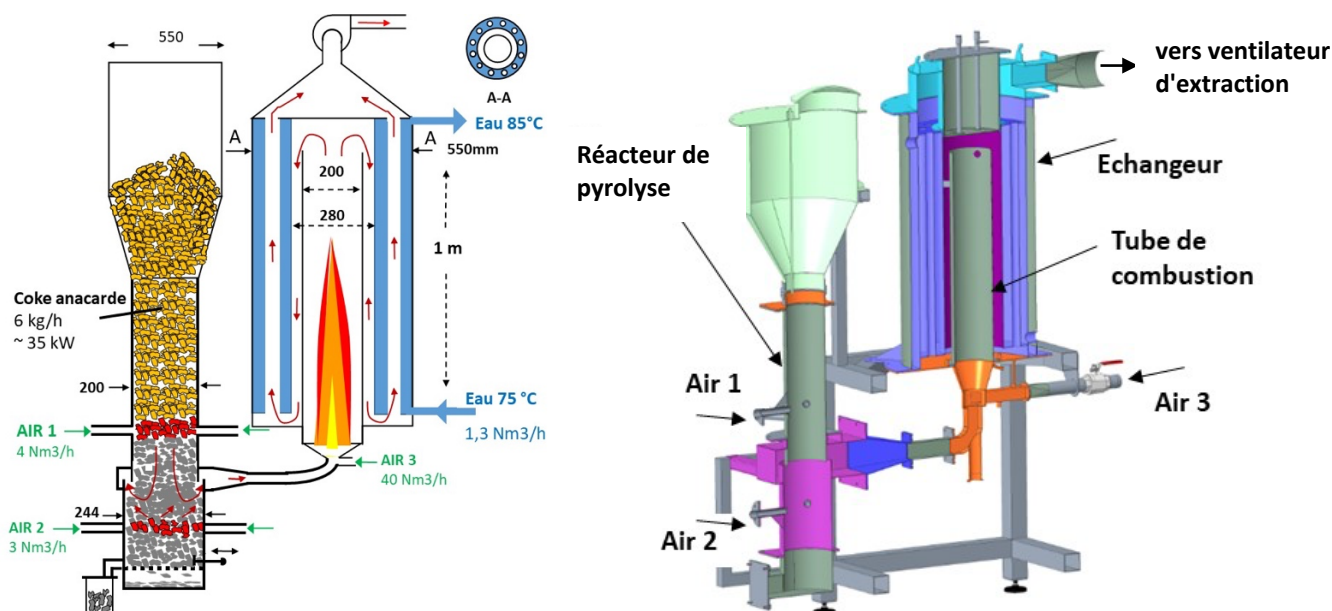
Schéma de principe et vue 3D en coupe de la chaudière
